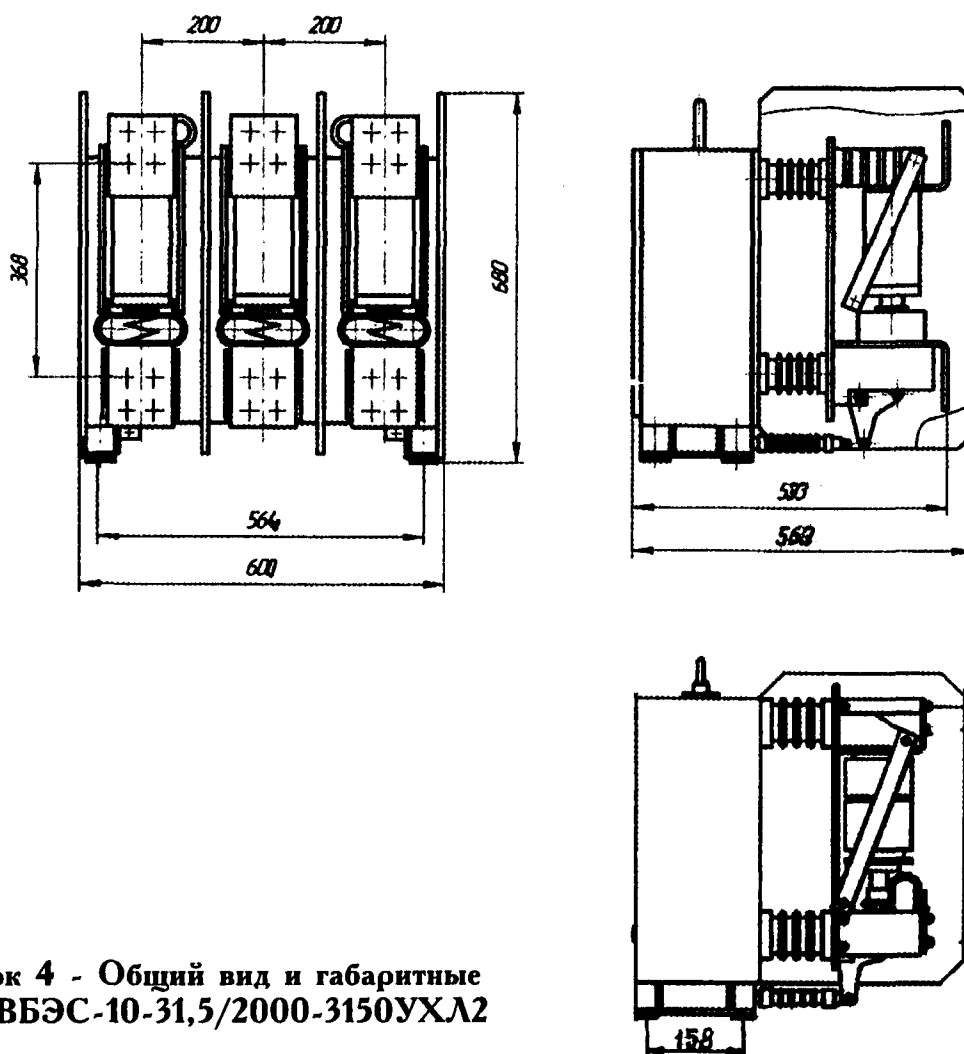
Общий вид и габаритные размеры ВБЭС-10-31,5/2000-3150УХЛ2
